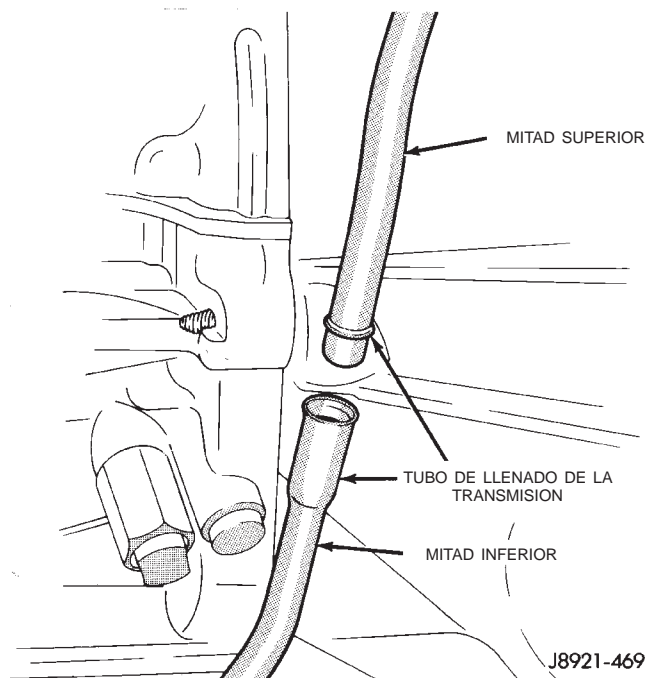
Tubo de llenado de la transmisión (de dos partes)
